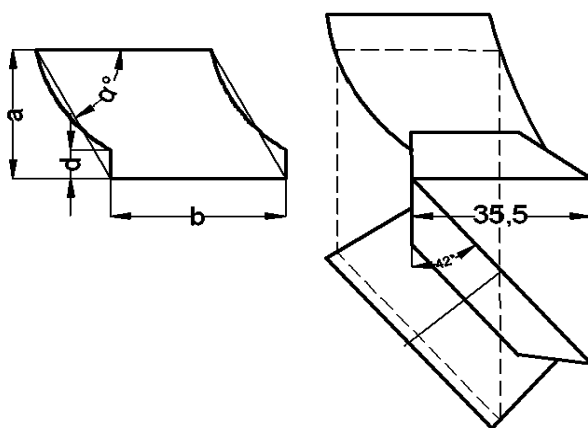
Схема симметричного плужного рабочего органа ромбовидного типа с двумя полевыми досками
